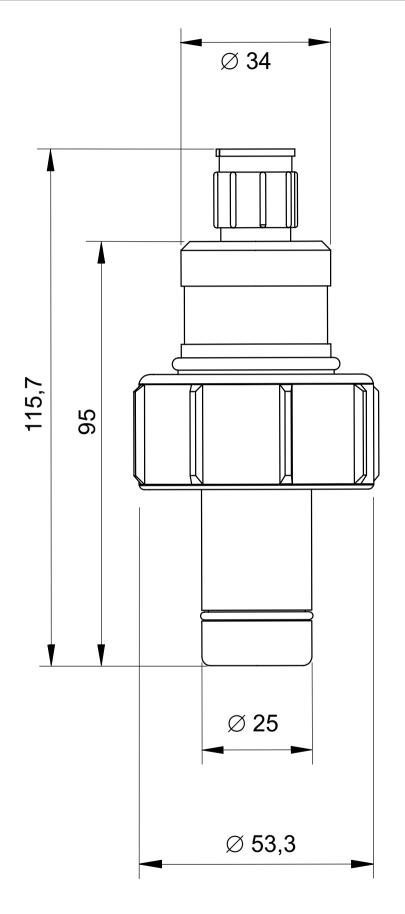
Desenho das dimensões do InPro 7100-25/7104-25 com 4 eletrodos
